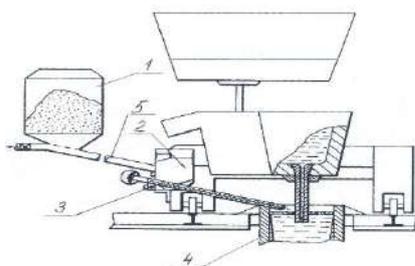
Конвейерное устройство для подачи порошковых смесей в кристаллизатор [7]: 1- накопительный бункер; 2- промежуточный бункер; 3- шнековый конвейер; 4-кристаллизатор; 5- ленточный конвейер
